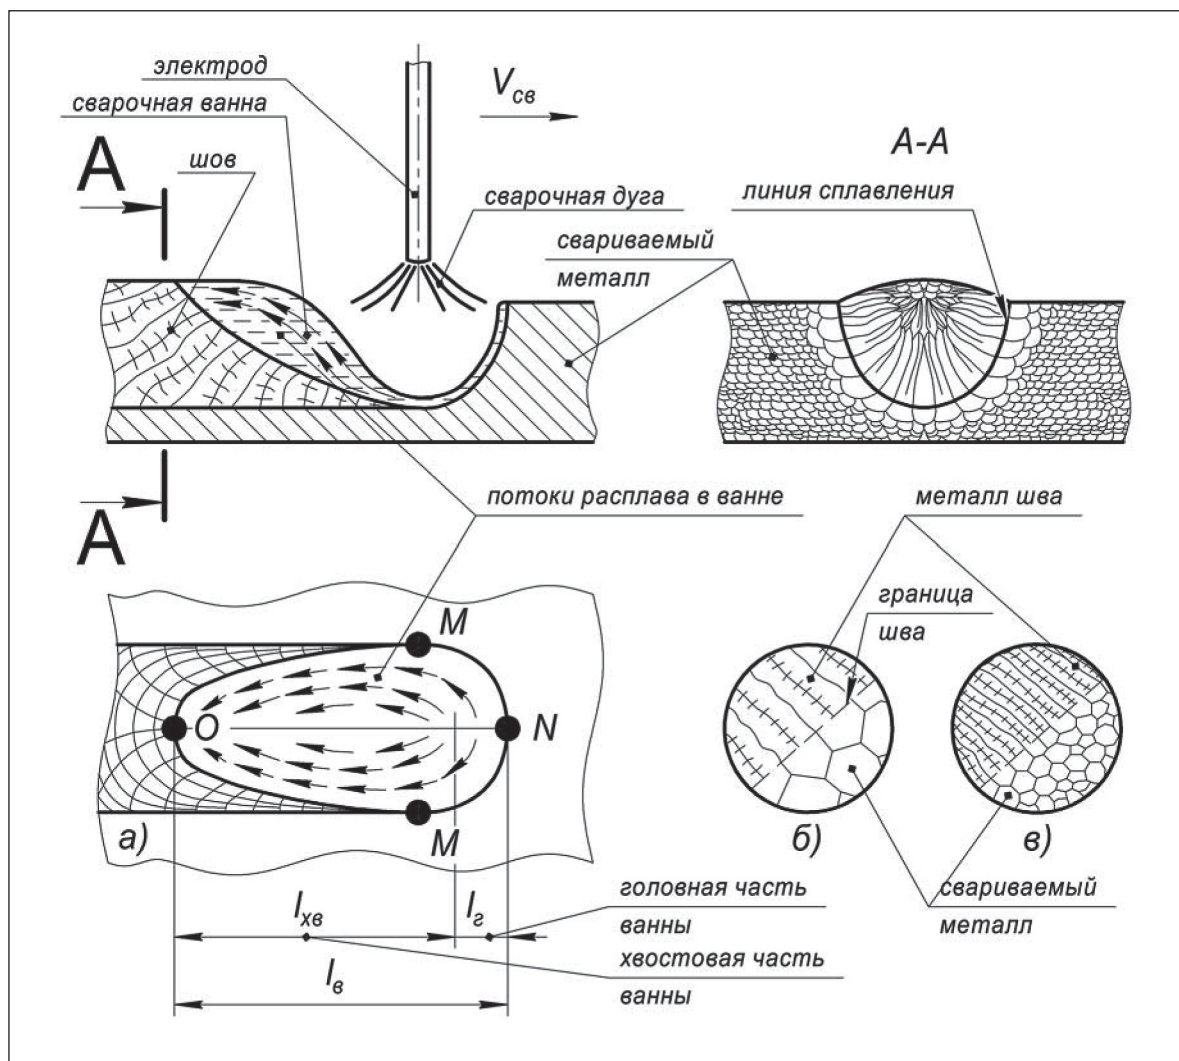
Схема образования шва дуговой сварки (а), формирование структуры шва при сварке аустенитной стали с крупным (б) и (в) мелким зерном: l_r , $l_{хв}$, l_b – длина головной части, хвостовой и общая длина сварочной ванны; $V_{св}$ – направление движения сварочной дуги; MNM – и MOM – фронт плавления и кристаллизации; стрелками обозначены потоки расплава в ванне
